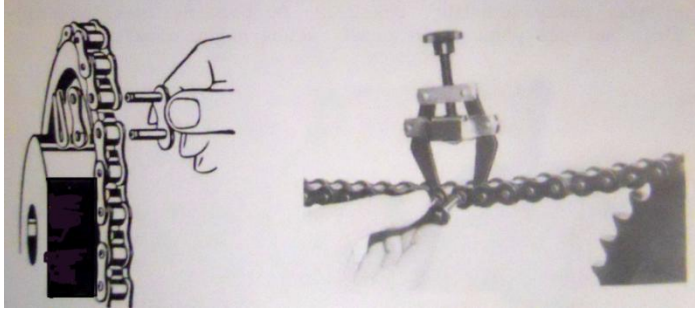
43. Zincir uçlarının birleştirilmesi [3]
